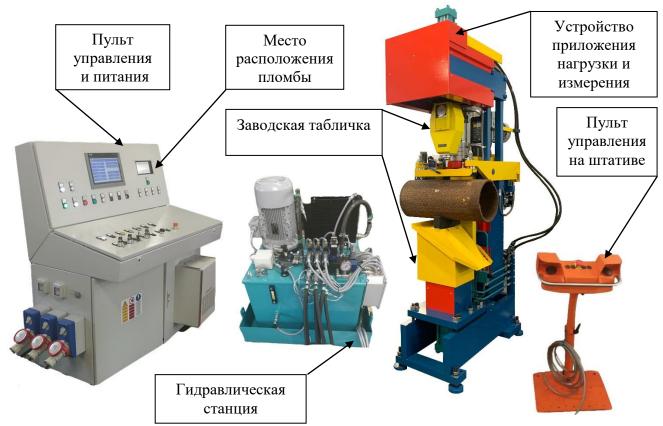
Общий вид твердомера BRE/AUT SOR
